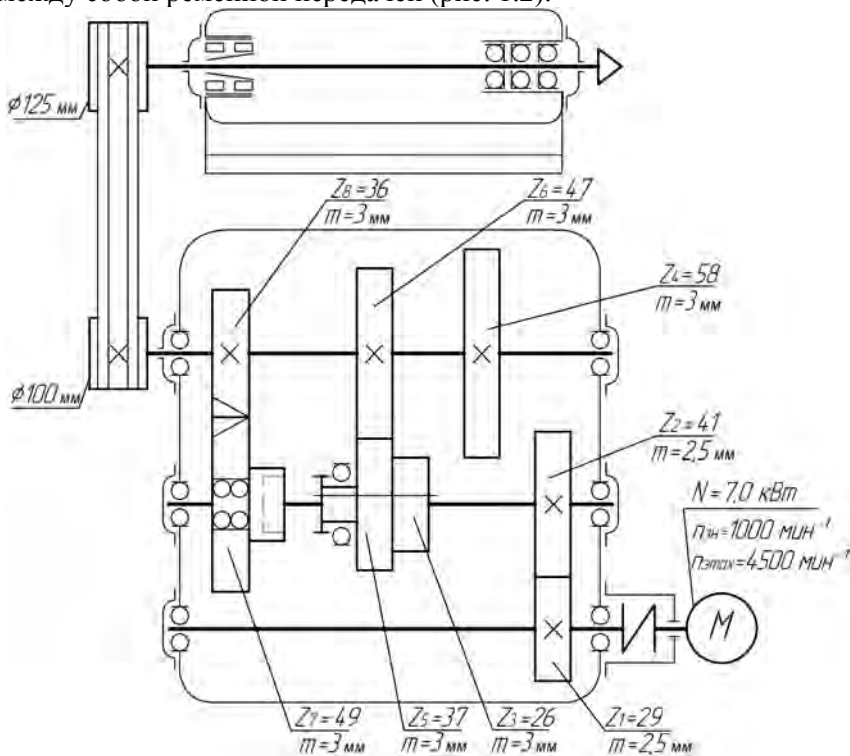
Кинематическая схема привода главного движения токарного станка с ЧПУ с автономной шпиндельной бабкой и коробкой скоростей с фланцевым электродвигателем
